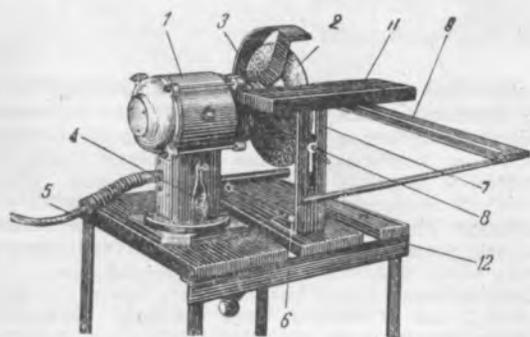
Приспособление к электроточилу И-138А — для заточки поперечных и лучковых пил: 1 — электроточило; 2 — точи́льный круг; 3 — предохранительный кожух; 4 — выключатель; 5 — провод электросети; 6 — нижняя часть передвижного столика; 7 — вертикальная стойка передвижного треугольного стола; 8 — закрепительный болт вертикальной стойки; 9 — передвижной треугольник столика; 11 — доска столика для точки пил, ножей; 12 — деревянная подставка станка.
